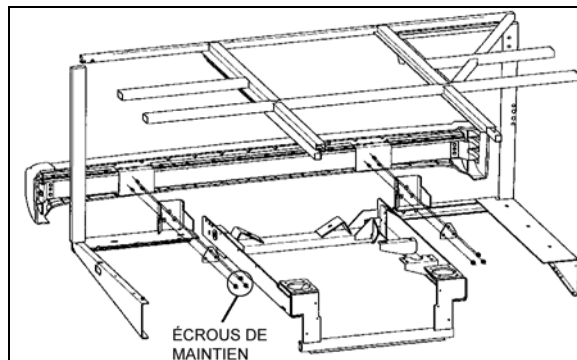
ENSEMBLE DU PARE-CHOCS ARRIÈRE
